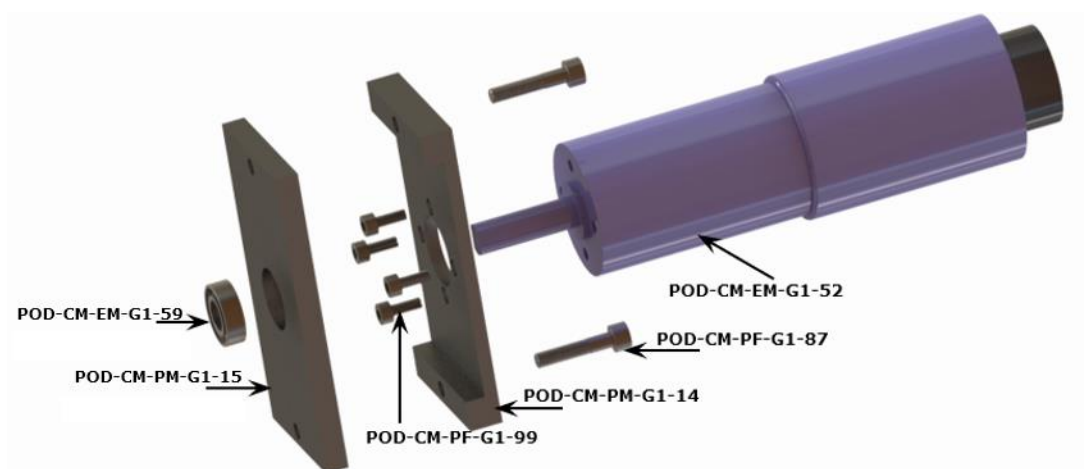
Parte inferior del mecanismo de movimiento principal
